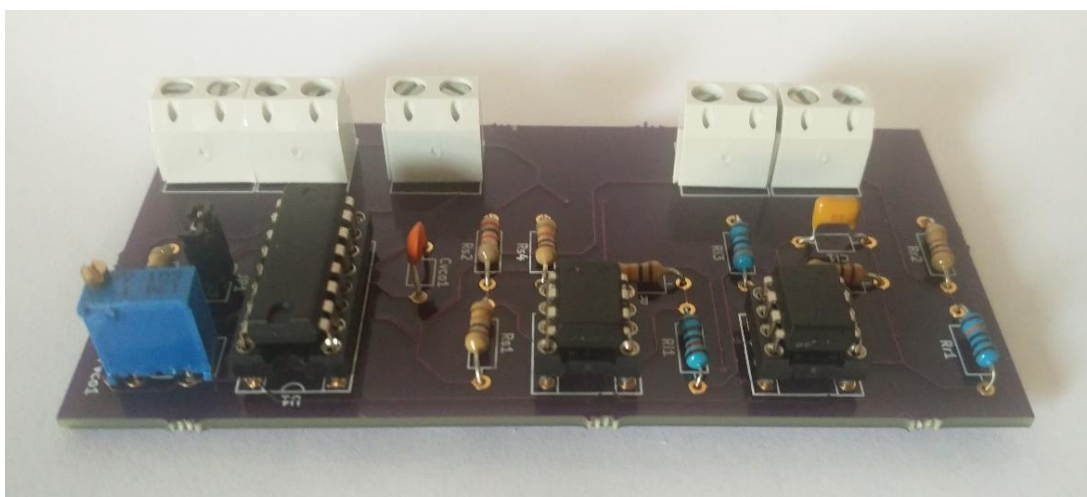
Placa generadora de señales con todos los componentes soldados.
